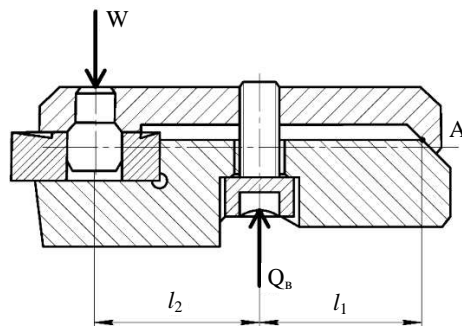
Расчётная схема рычажного механизма в резцовом блоке
